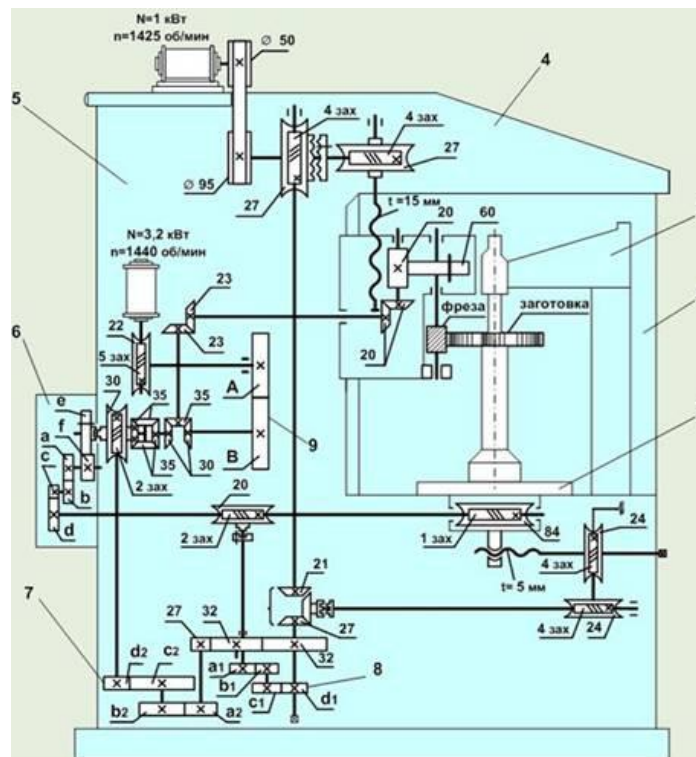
Кинематическая схема зубофрезерного полуавтомата мод. 5К301Ф с ЧПУ
